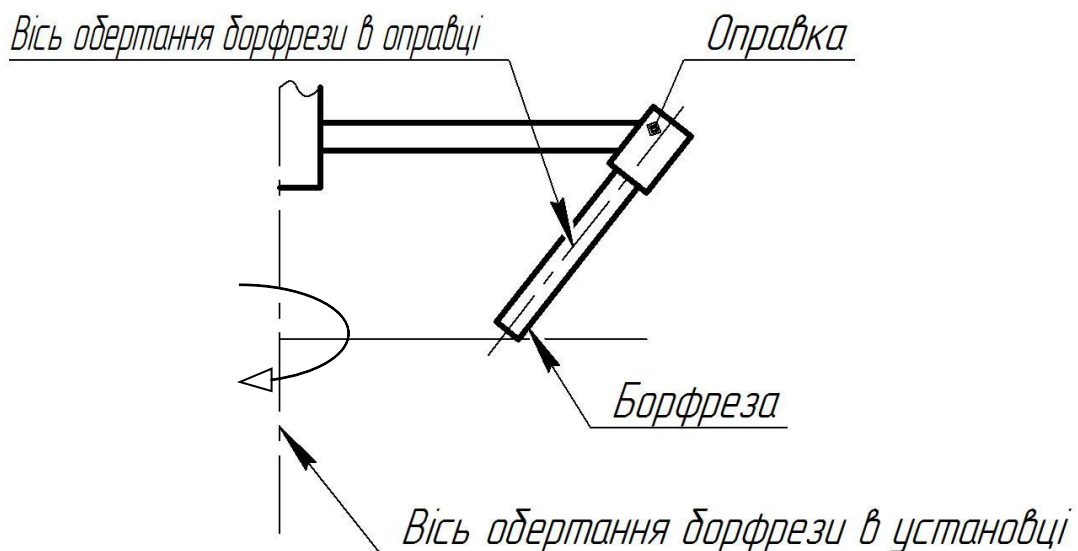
Схема розташування борфрез в робочій зоні під кутом ρ
